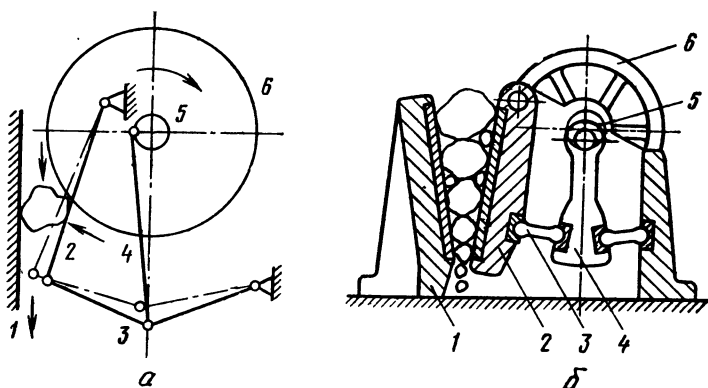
Камнедробилка щековая с приводом от шарнирной распорки и кривошипного механизма:
